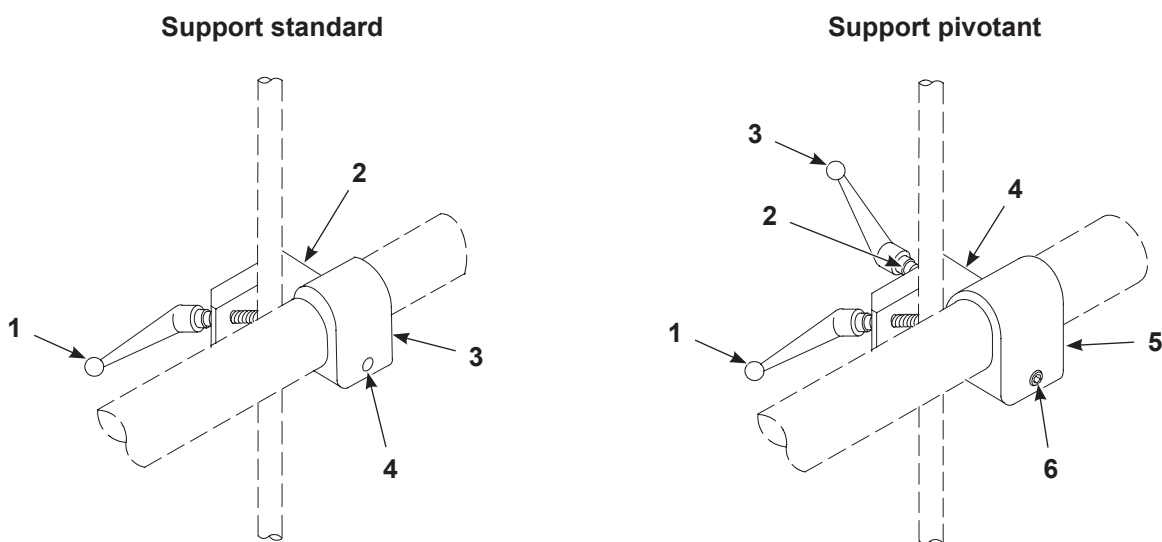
Supports à barre pour pistolets de pulvérisation à fixation sur tube
